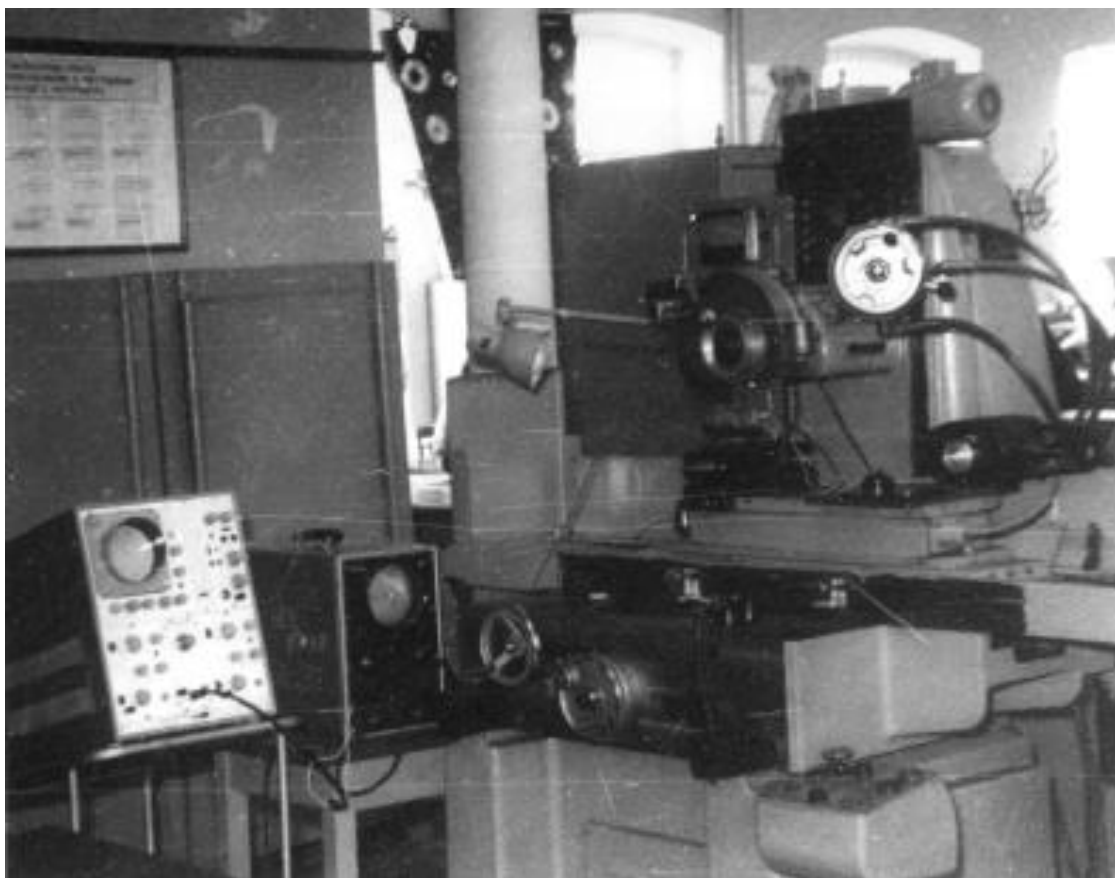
Общий вид установки для измерения усилий разрушения зерна
